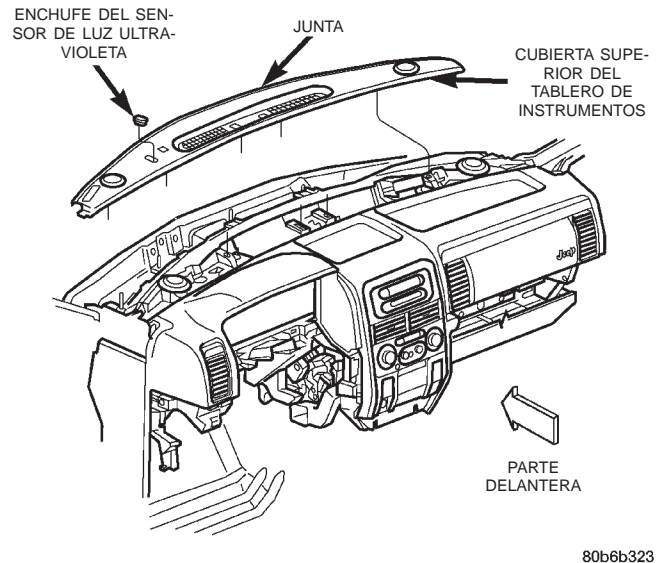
Desmontaje e instalación de la cubierta superior del tablero de instrumentos
